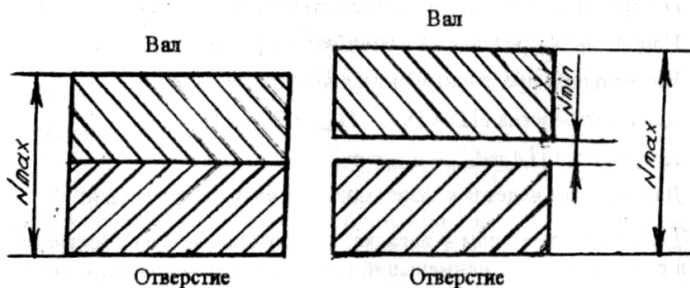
Схема полей допусков для посадки с натягом.
